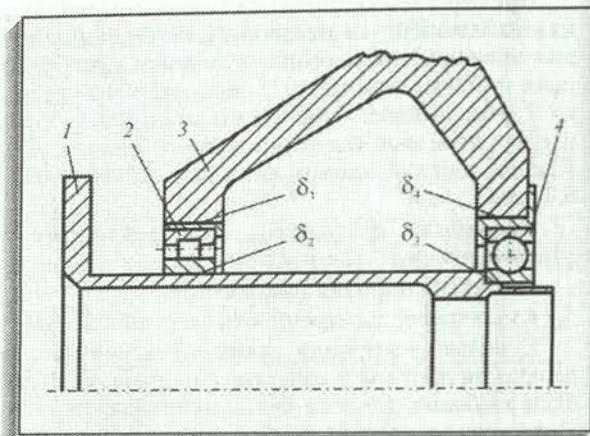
Схема установки вала винта в картере авиационного турбовинтового двигателя: 1 — вал винта; 2 — роликовый подшипник; 3 — картер двигателя; 4 — шариковый подшипник;  $\delta_1$  — посадка роликового подшипника на вал;  $\delta_2$  — посадка роликового подшипника в картер редуктора;  $\delta_3$  — посадка шарикового подшипника на вал;  $\delta_4$  — посадка шарикового подшипника в картер редуктора
